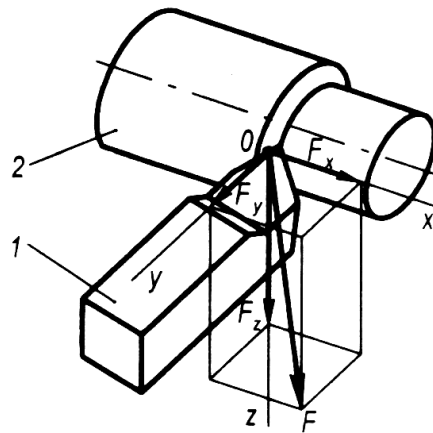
Сила різання під час точіння F і її складові: F_z - головна складова сили різання; F_x - осьова складова; F_y — радіальна складова сили різання; 1 - різець; 2 - заготовка
